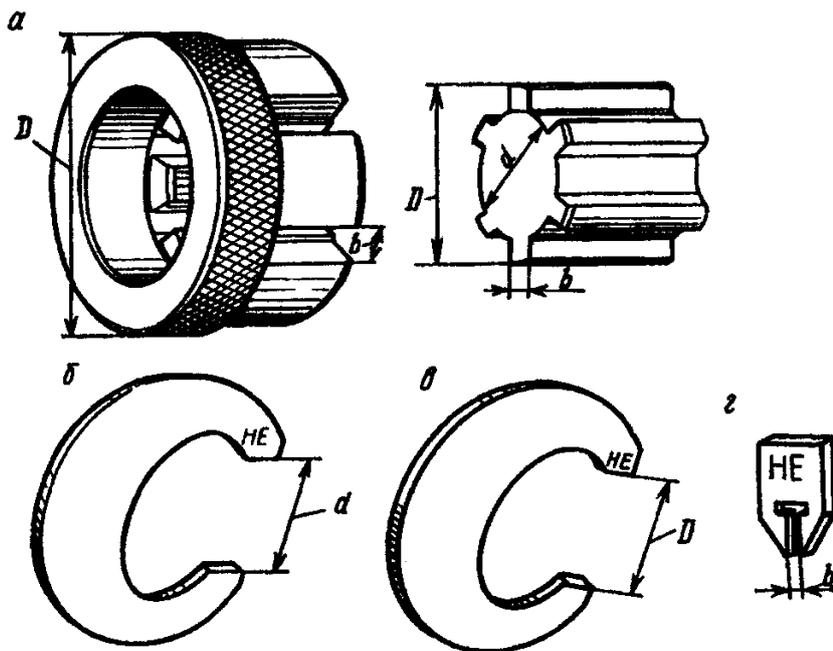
Калибры для контроля шлицевого прямобочного вала:
